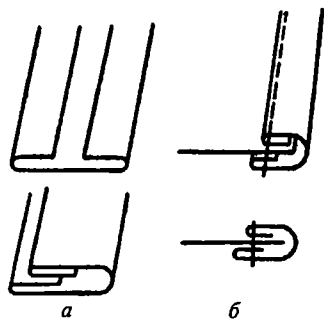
Окантовочный шов с закрытыми срезами на машине без приспособления с предварительным зауживанием полоски для окантовки
